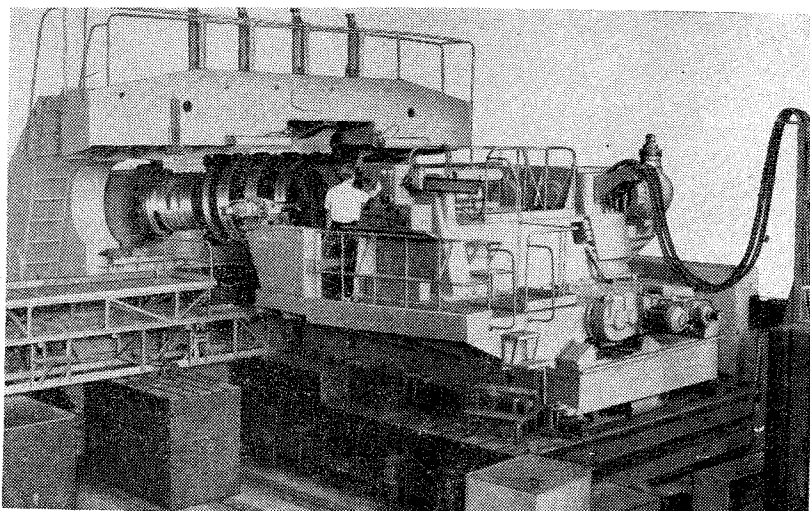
Общий вид станка НР-6 с установленной на нем верхней половиной цилиндра
